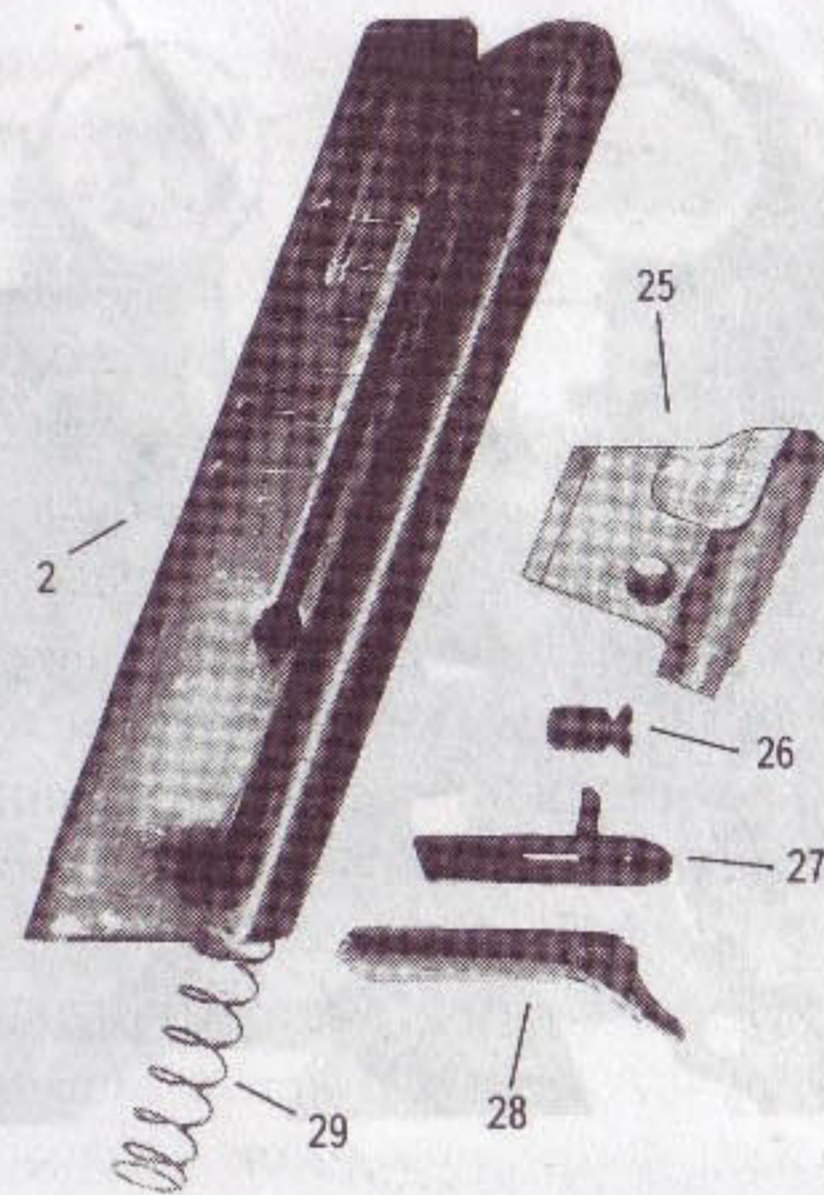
Разборка магазина: извлечь замыкатель (27); извлечь пружину подавателя (29); опустить вниз подаватель (25); извлечь кнопку подавателя (26)
